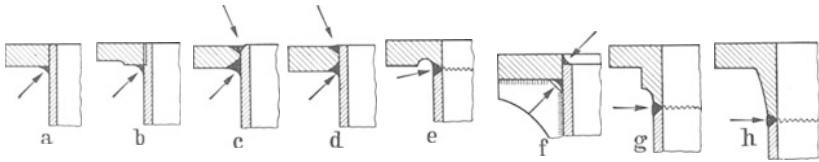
Schweißungen von Rohrflanschen.
